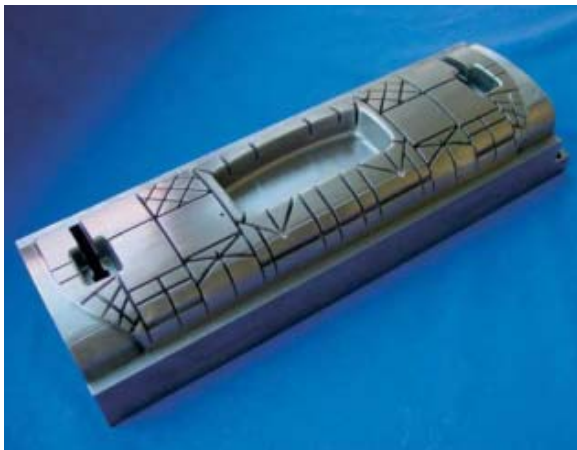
ecoMold Referenzwerkzeug (420 x 140 x 75 mm³).
